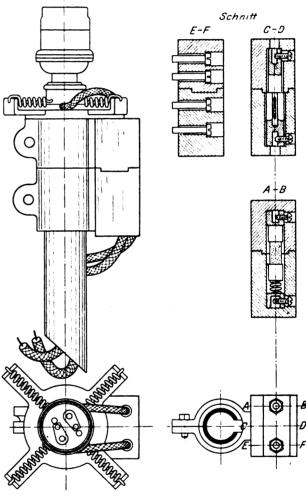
Weichen-Signallampe, Bauart Steinbardt.
